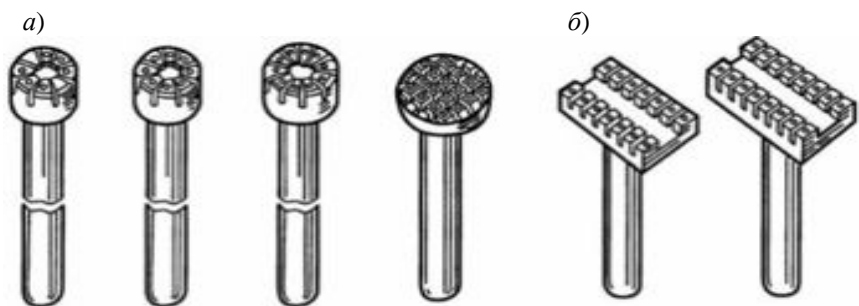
Насадки к электропаяльникам для выпайки микросхем в круглых (а)
